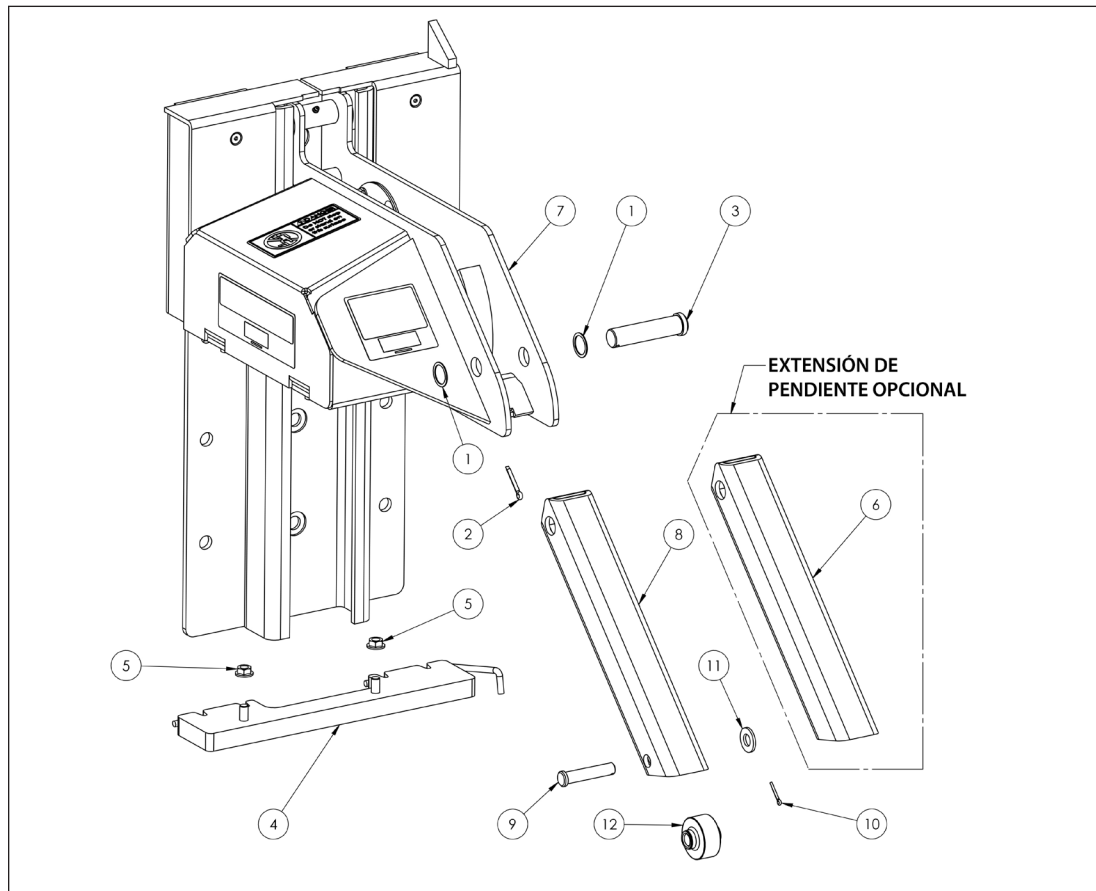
FIGURA AO—CONJUNTO DE EXTENSIÓN DE PENDIENTES
